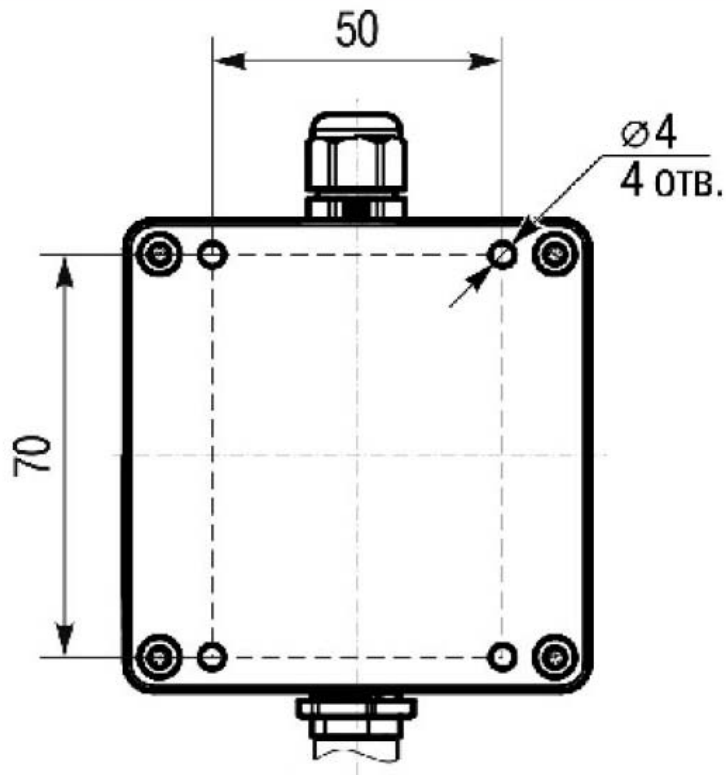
Корпус ОВЕН ПТВ100.
